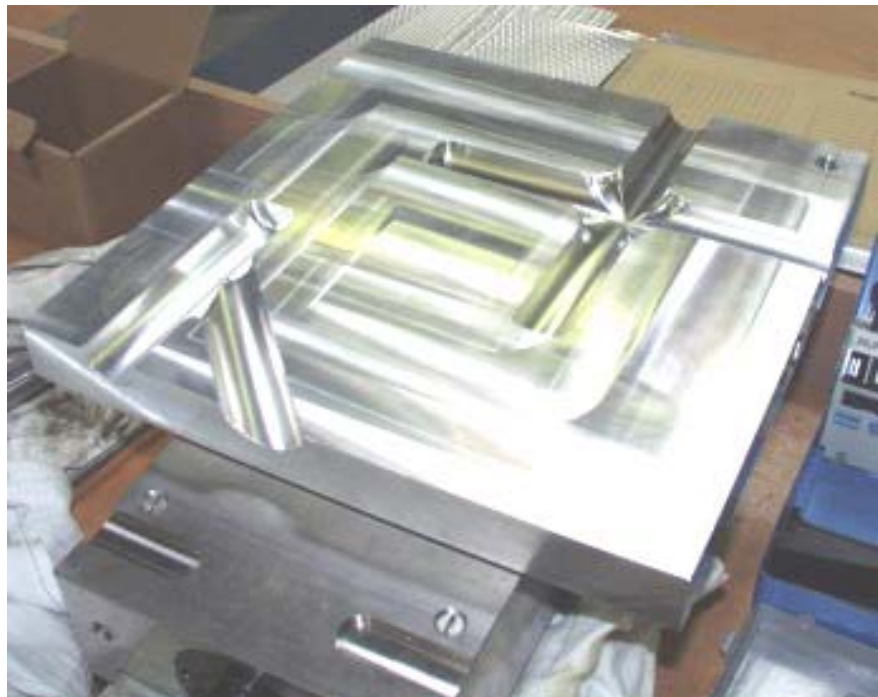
Werkzeughälfte mit gefrästen Knotengeometrien
